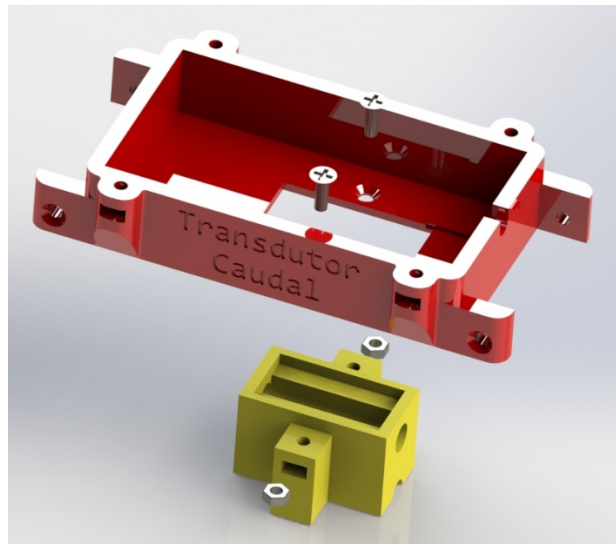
Vista explodida da montagem entre o suporte e a caixa
